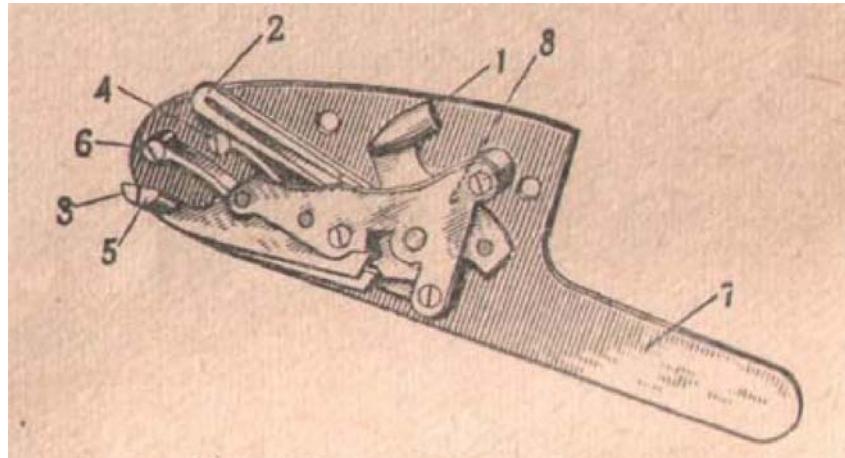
Ложно-подкладной замок (ружья модель ТС-1): 1 - курок; 2 - боевая пружина; 3 - шептало; 4 - пружина шептала; 5 - перехватыватель курка; 6 - пружина перехватывателя; 7-замочная доска; 8 - замочная стойка (боевая личинка)
